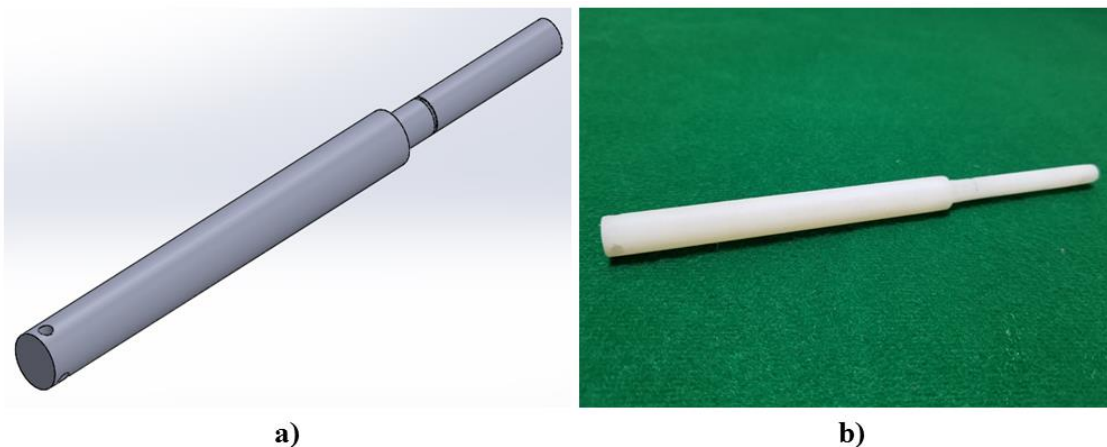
a) Eje principal de agitador diseñado, b) Eje del agitador maquinado
